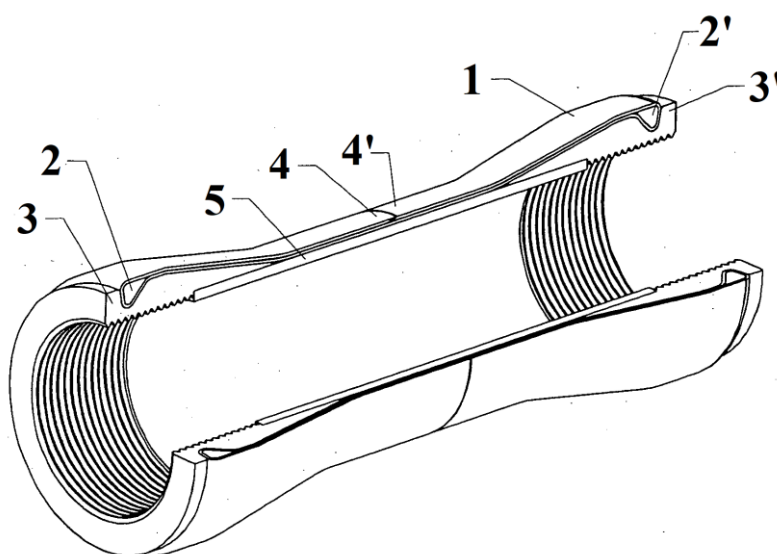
Разрез композитной трубы с прикрепленными концевыми фитингами
